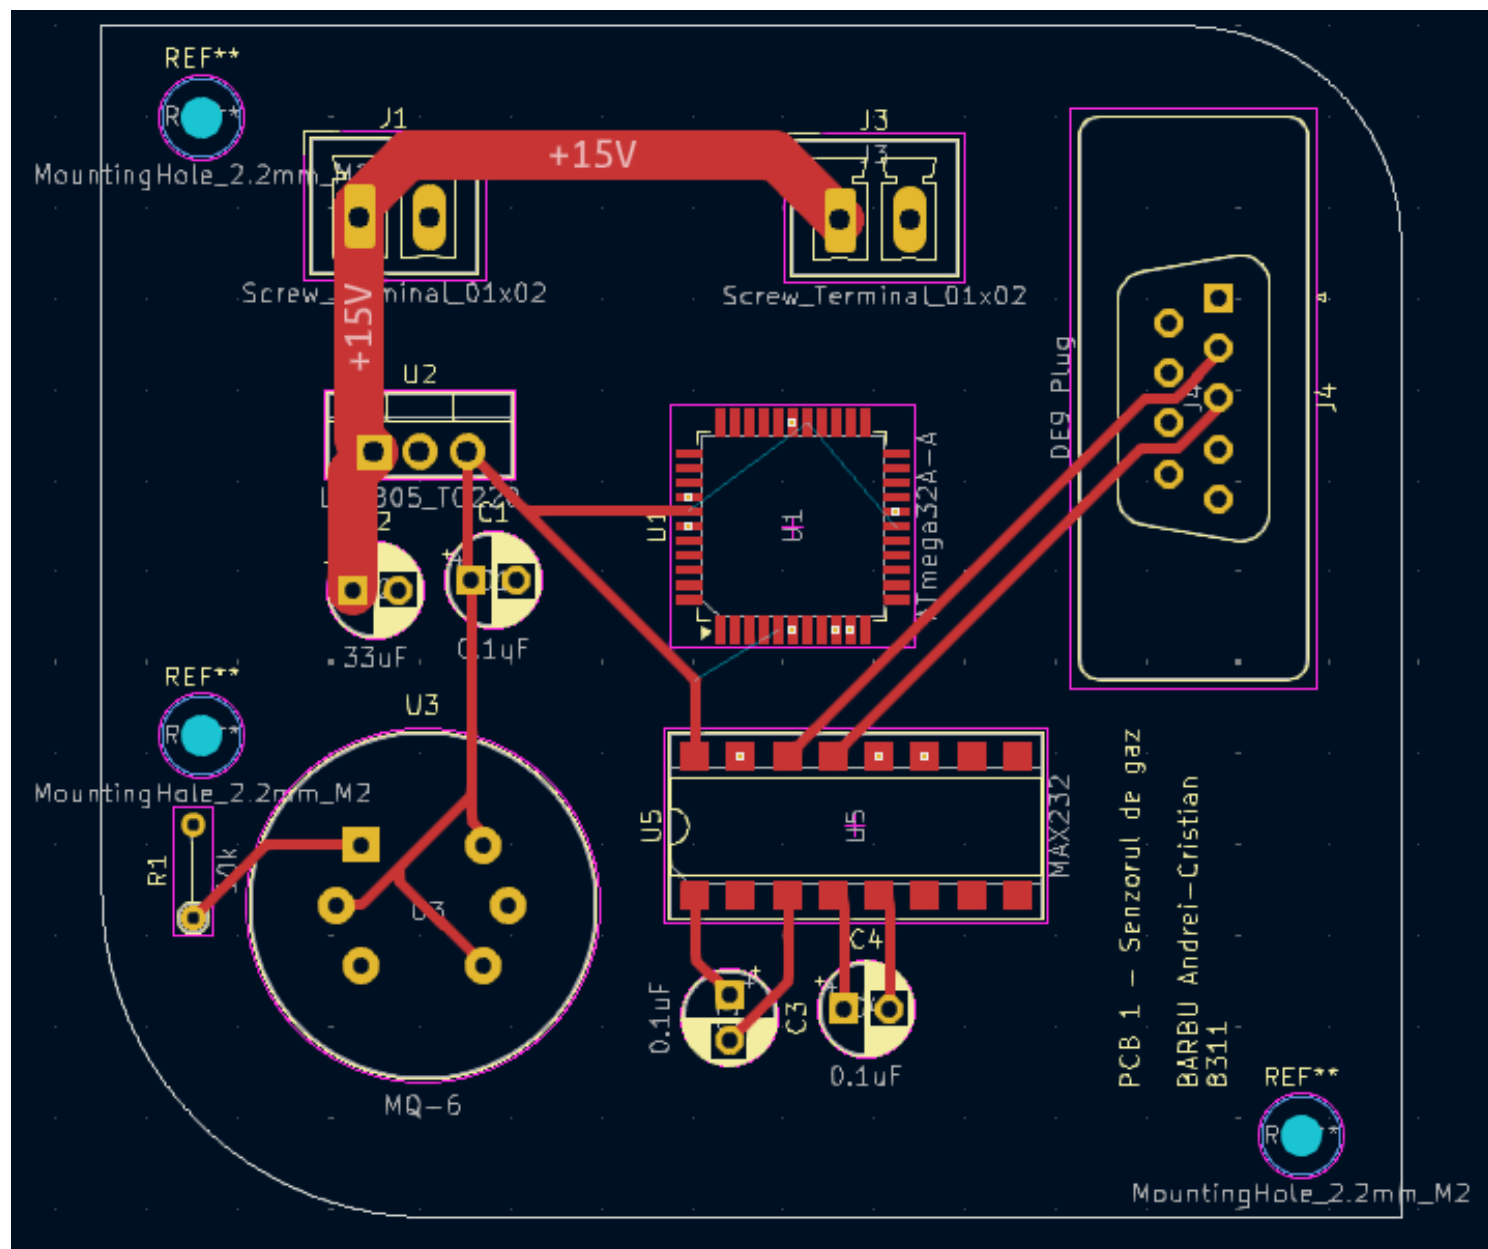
Cablaj imprimat din KiCad (Front Layer)
